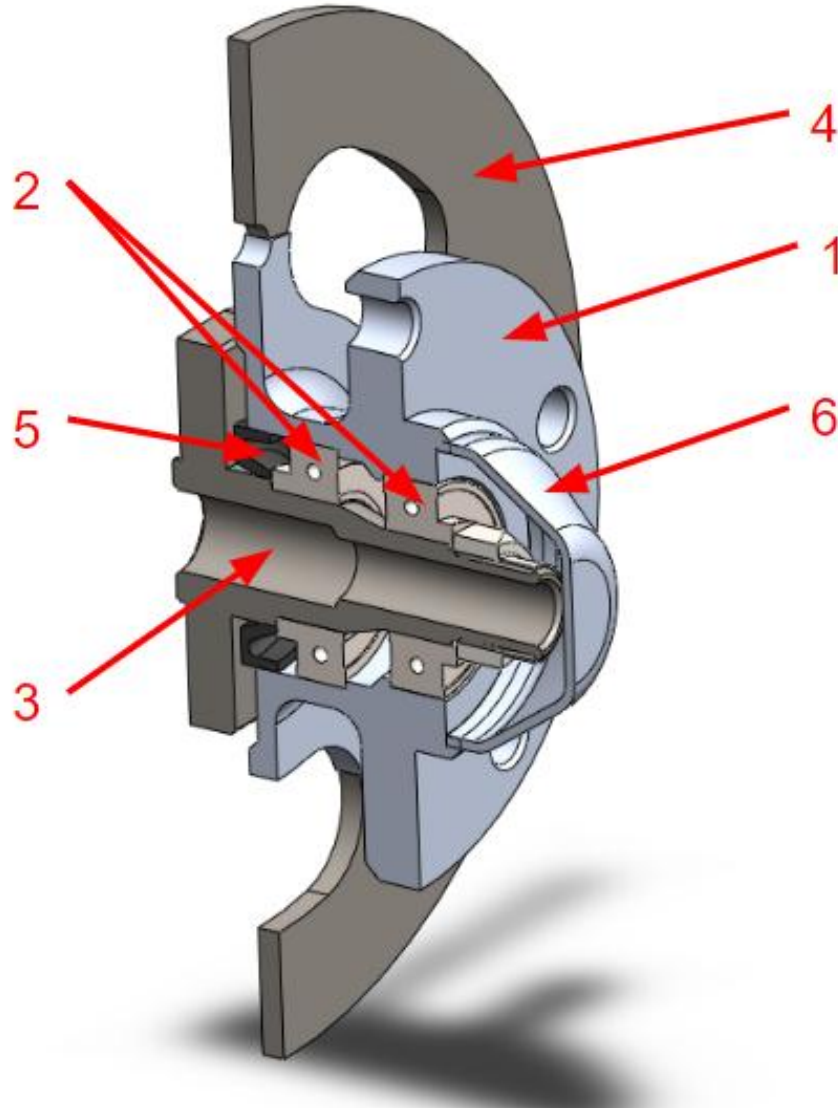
Маточинний вузол переднього поворотного кулака
